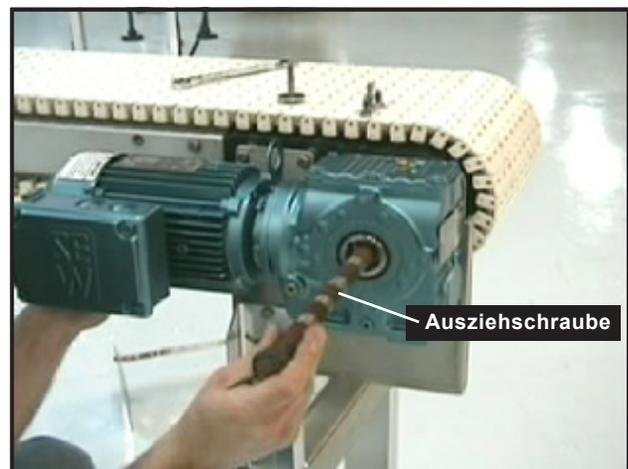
Ausziehschraube einfügen um den Getriebekasten vom Schaft zu entfernen
